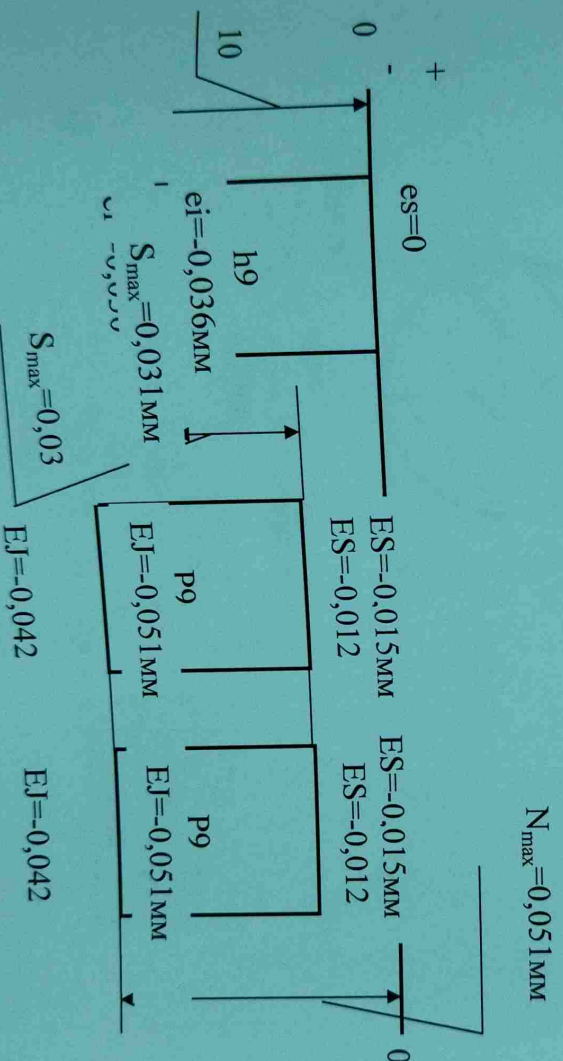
Схема расположения полей допусков для шпоночного соединения.
